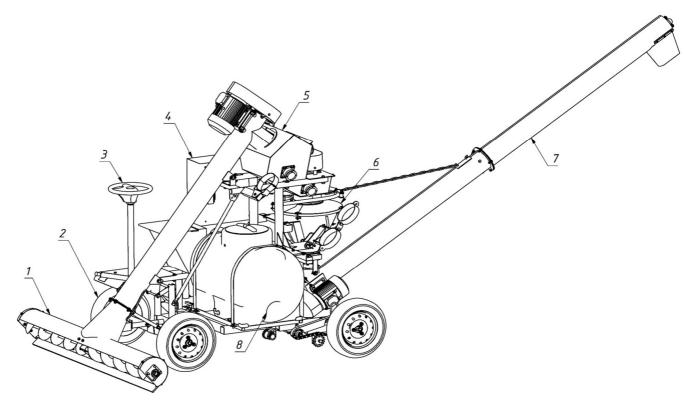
Общий вид ПС-20 в рабочем положении
